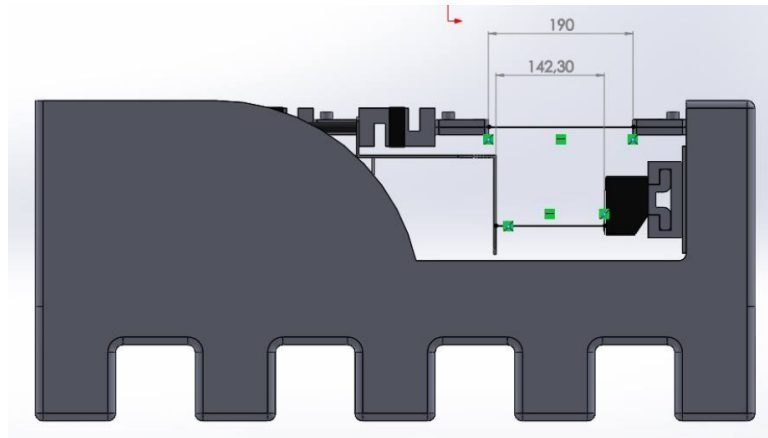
Algumas dimensões da máquina de ensaios de impacto
